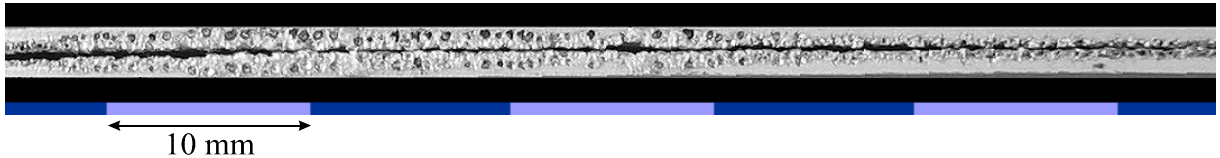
Querschnitt (aufgeklappt, Draufsicht) einer Aluminium-Schweißnaht. Man erkennt eine starke Porenbildung sowie ein mangelhaftes Durchschweißen im rechten Bereich der Naht.
